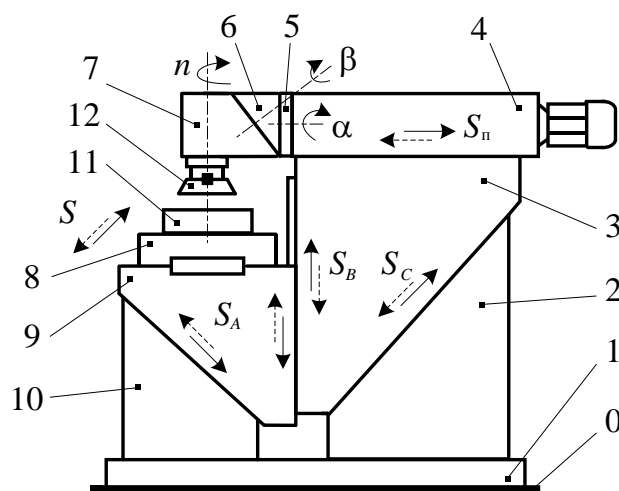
Общий вид универсального фрезерного станка нетрадиционной компоновки:
